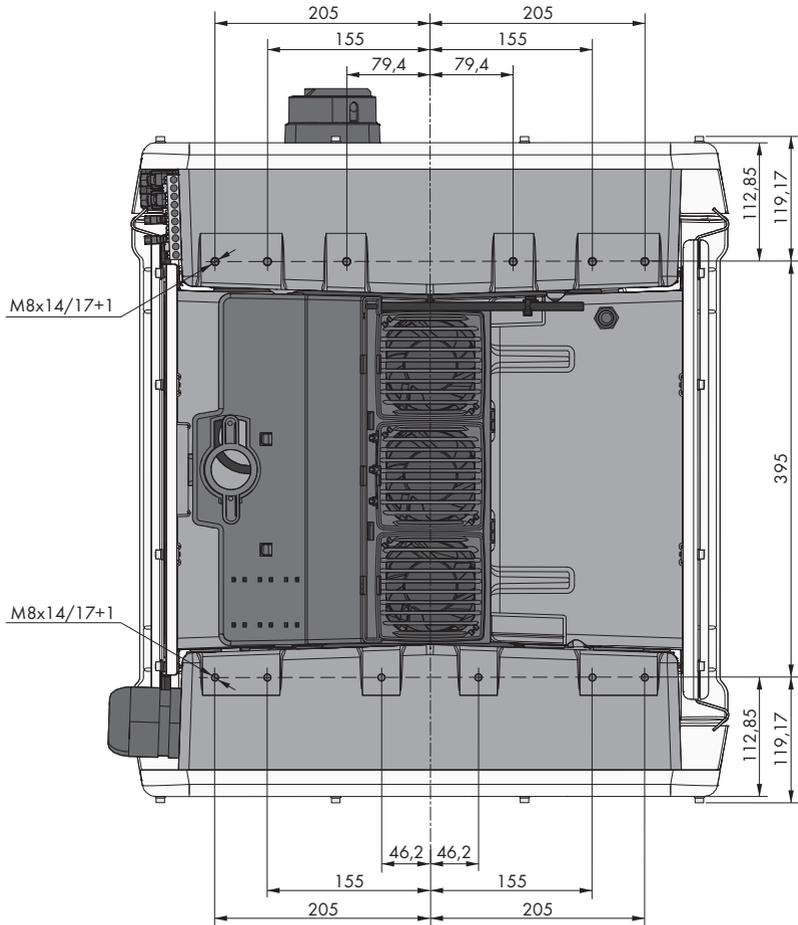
Posição dos pontos de fixação (dimensões em mm)
